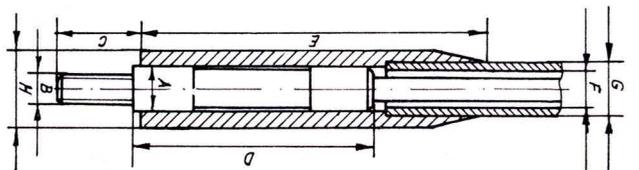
Beispiel für Lagerung biegsamer Wellen (Maße in mm)
